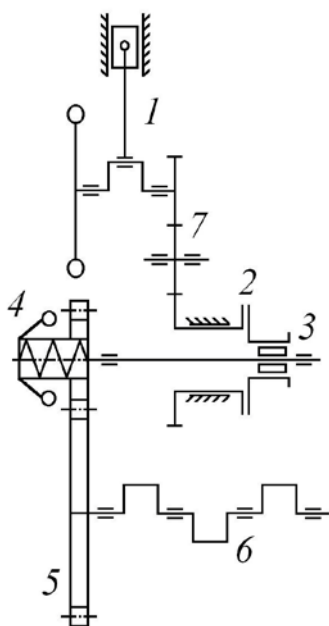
Схема пуска при помощи пускового двигателя:
